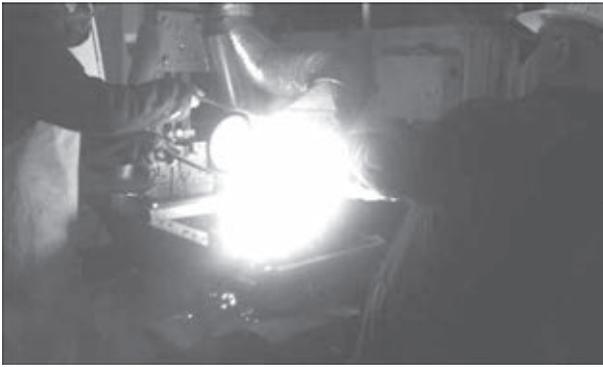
Заливка расплавленного шлака в токоподводящий кристаллизатор (жидкий старт)
